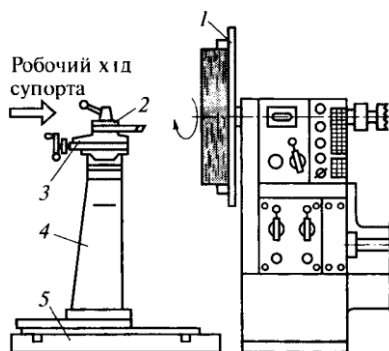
Приставний лобовий пристрій токарного верстата: 1 – планшайба; 2 – різцетримач; 3 – супорт; 4 – стійка; 5 – основа
